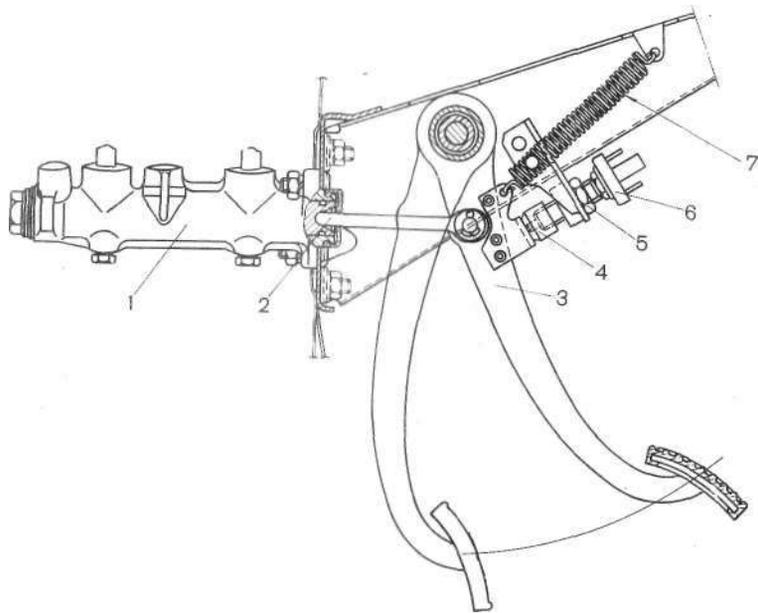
Педаль тормоза: 1 — главный цилиндр гидросистемы тормозов; 2 — толкатель; 3 — педаль тормоза; 4 — буфер выключателя стоп-сигнала; 5 — гайка упорного винта; 6 — выключатель стоп-сигнала; 7 — оттяжная пружина педали
